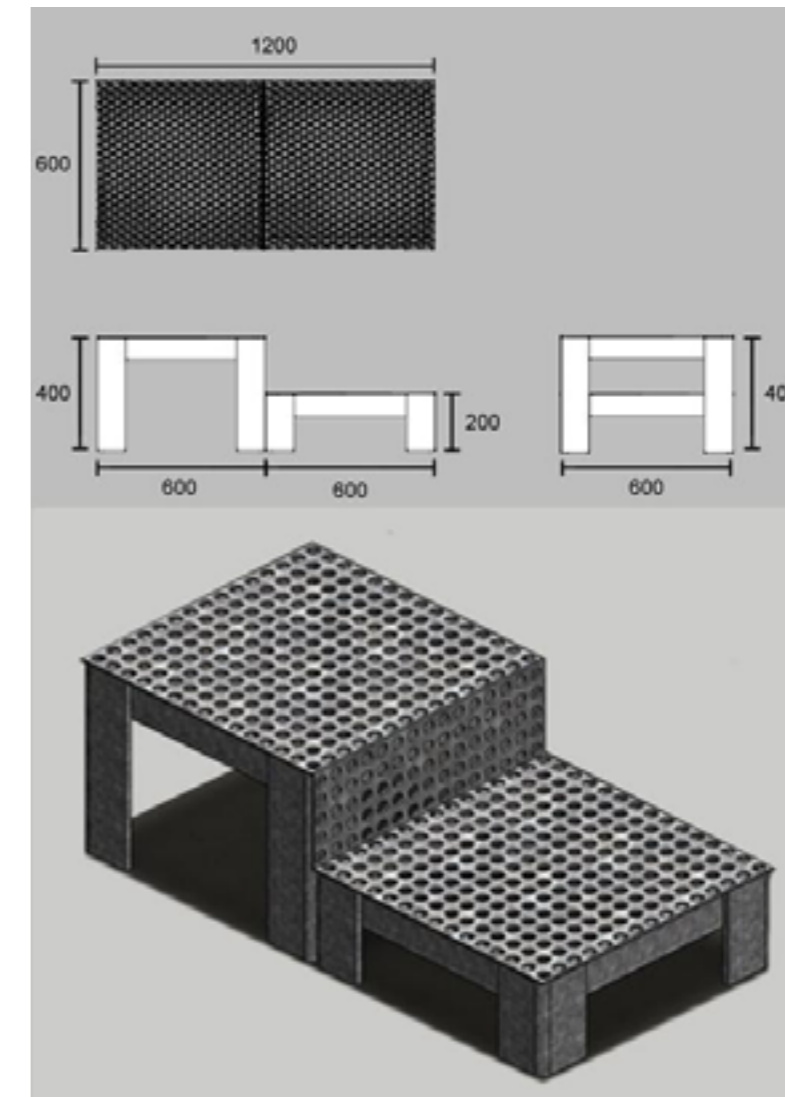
Detalhamento técnico (cotas em milímetros) e vista em perspectiva da plataforma.
